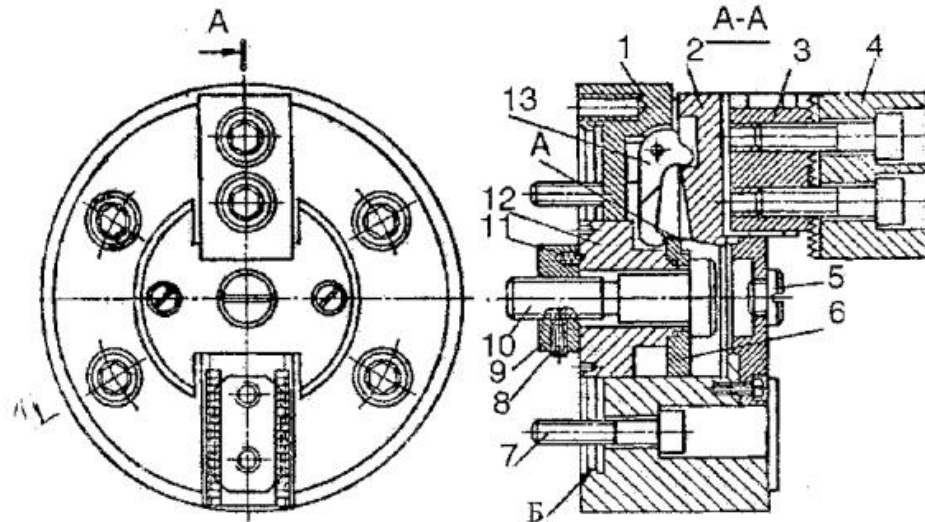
Конструкция клинорычажного двухкулачкового самоцентрирующего патрона с пневмоприводом; 1 – корпус; 2 – основания кулачков; 3 – сухари; 4 – сменные кулачки; 5 – заглушка; 6 – гайка; 7 – болт; 8 – стопорный винт; 9 – гайка; 10 – винт; 11 – шариковый стопор; 12 – втулка; 13 – рычаг.
